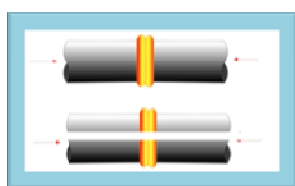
Corte transversal de la unión soldada por FRW
